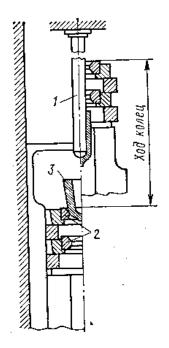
Схема штампа для вытяжки полой поковки через подвижные кольца: 1 – пуансон; 2 – кольца; 3 – заготовка
